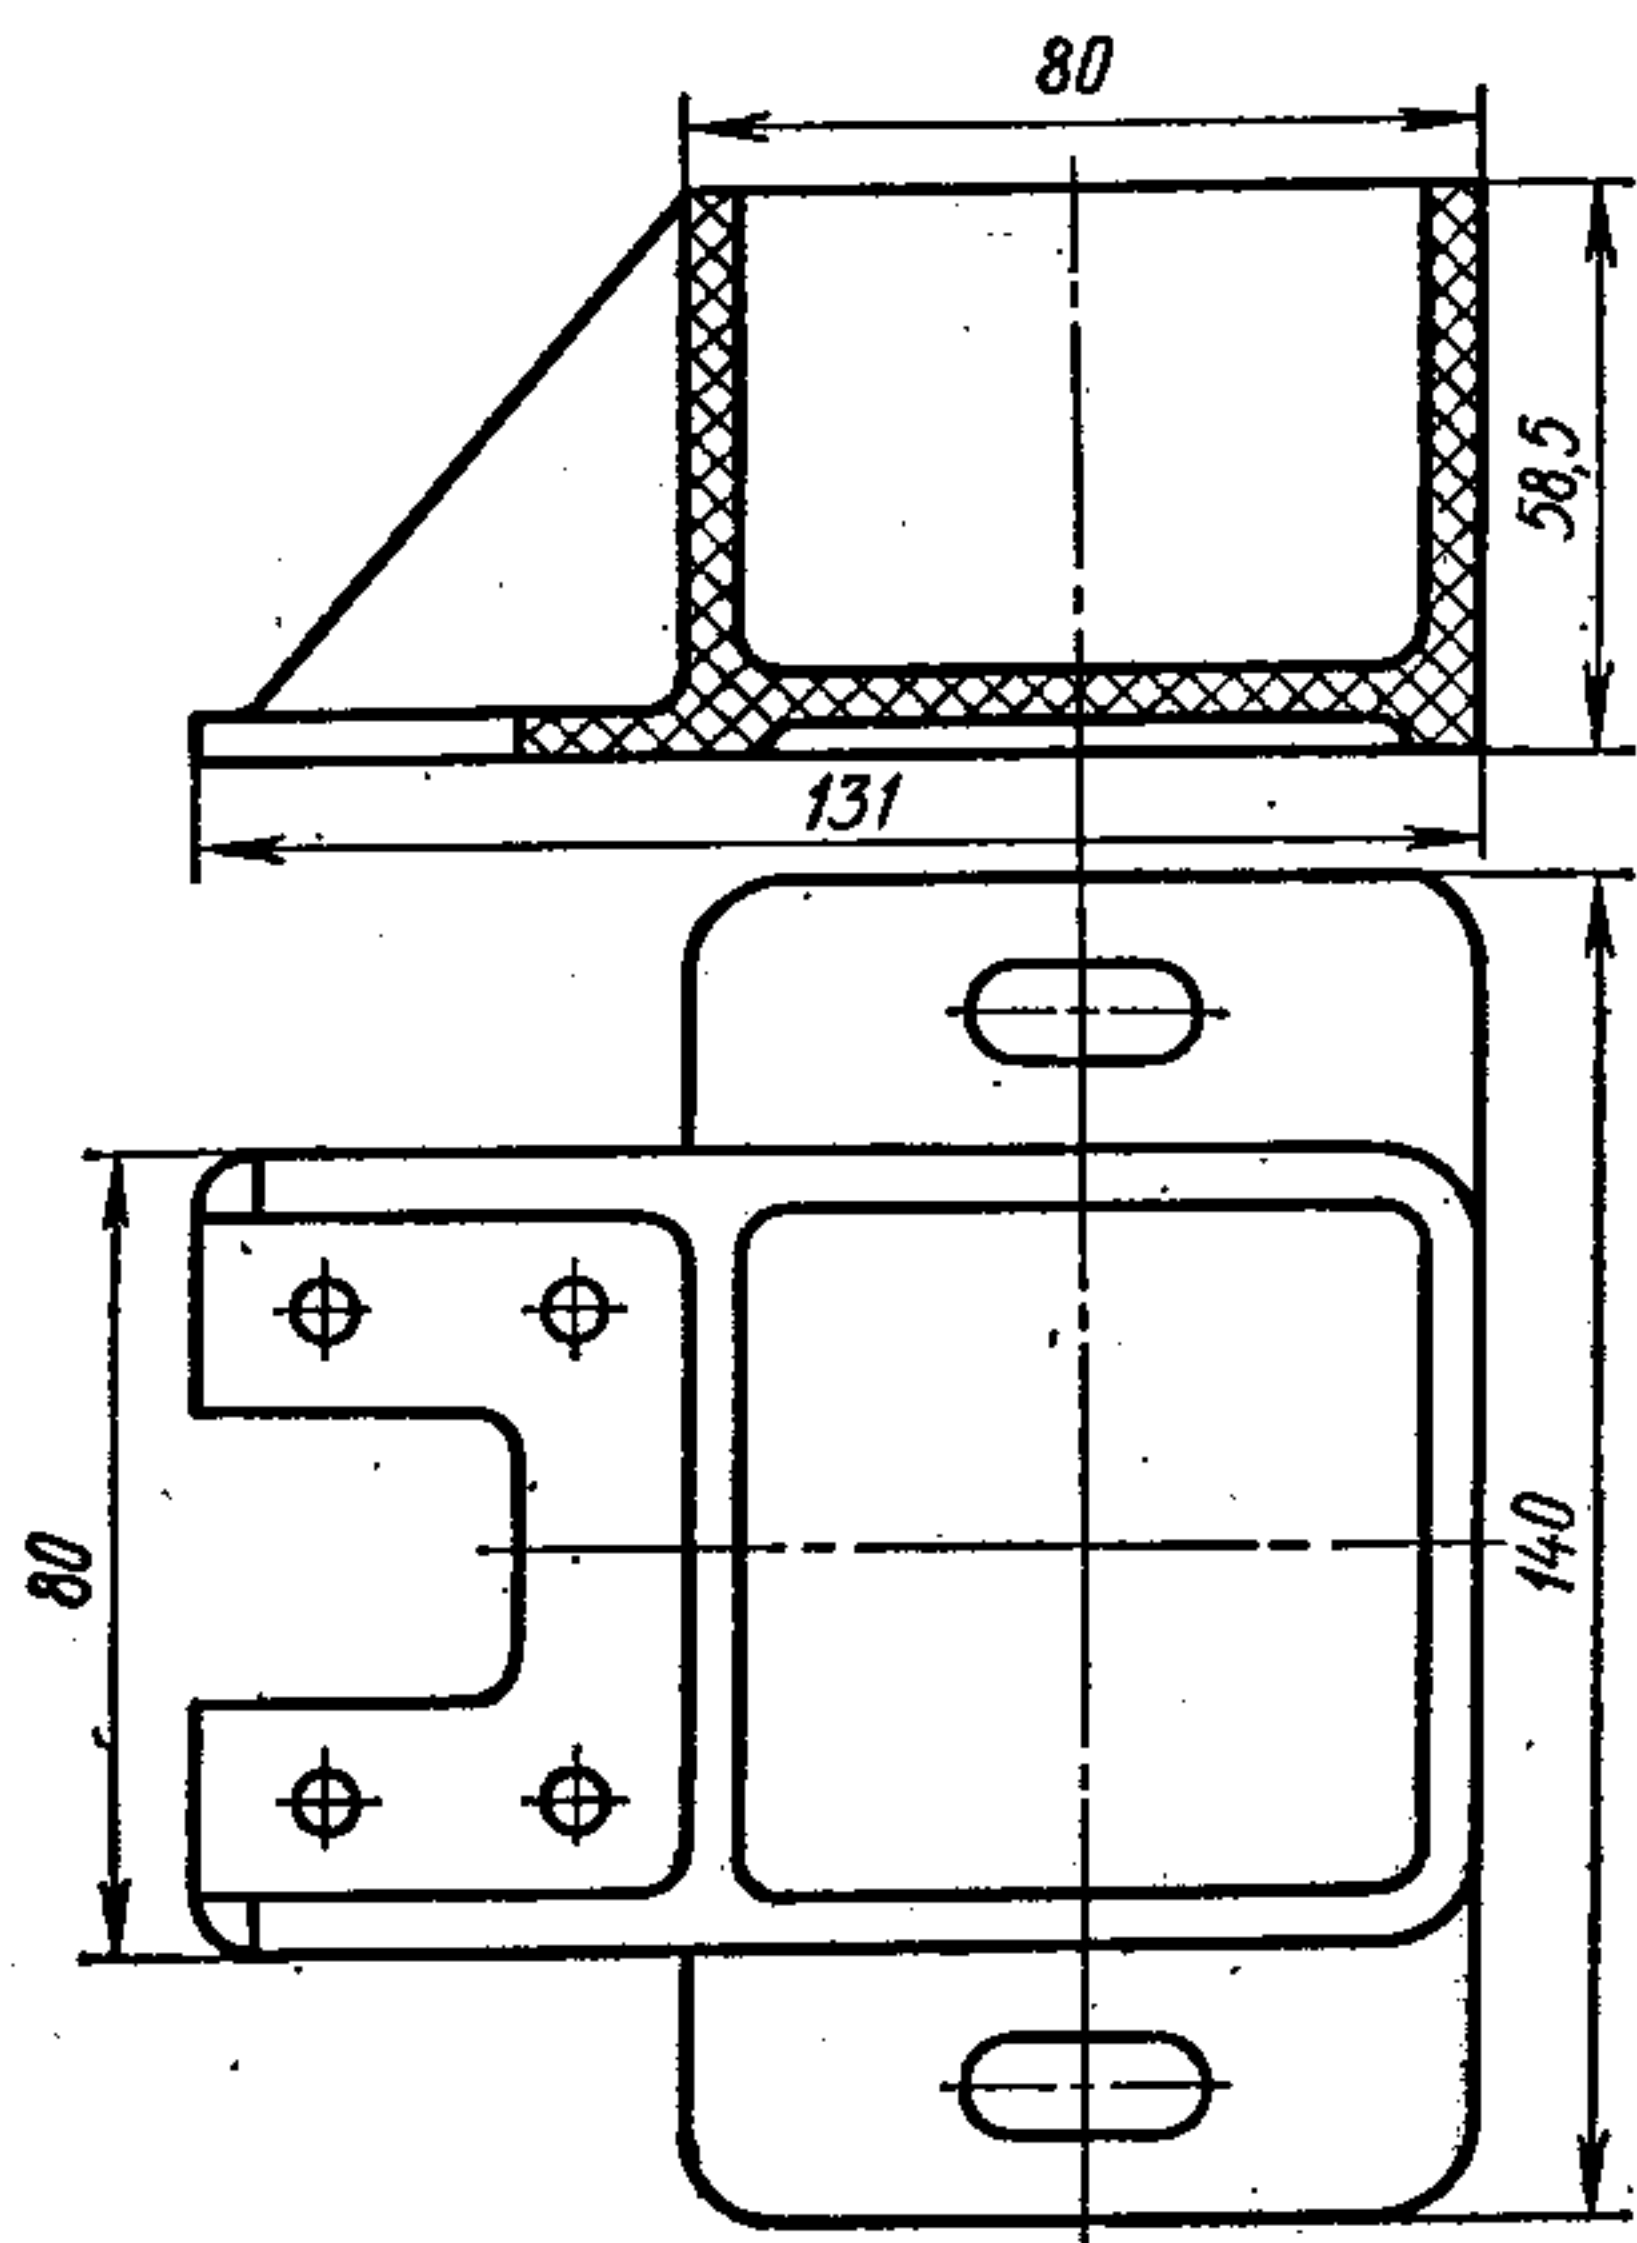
Ребра жесткости на корпусе смазывающего устройства (фенопласт)
